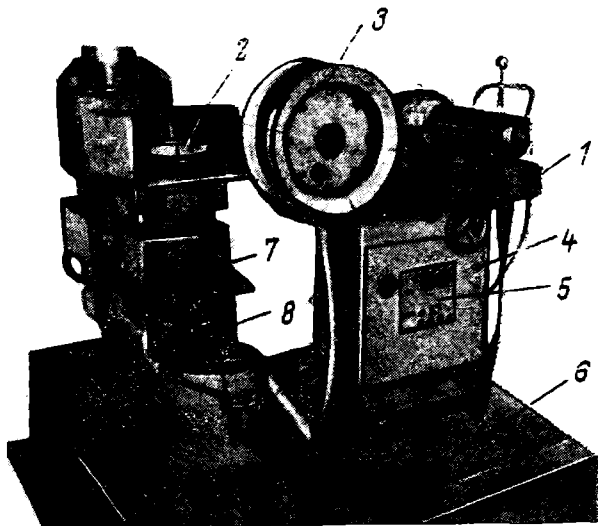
Копировально-шероховальный станок типа ШШК-64:
